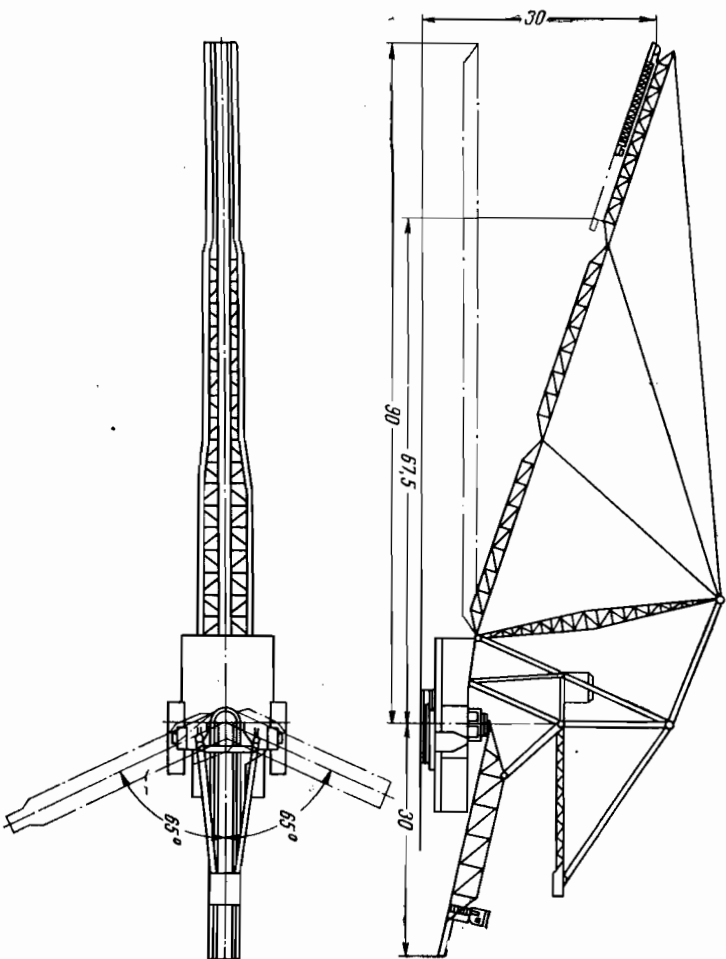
Схема шагающего консольного отвальобразователя ОП-4500/90
